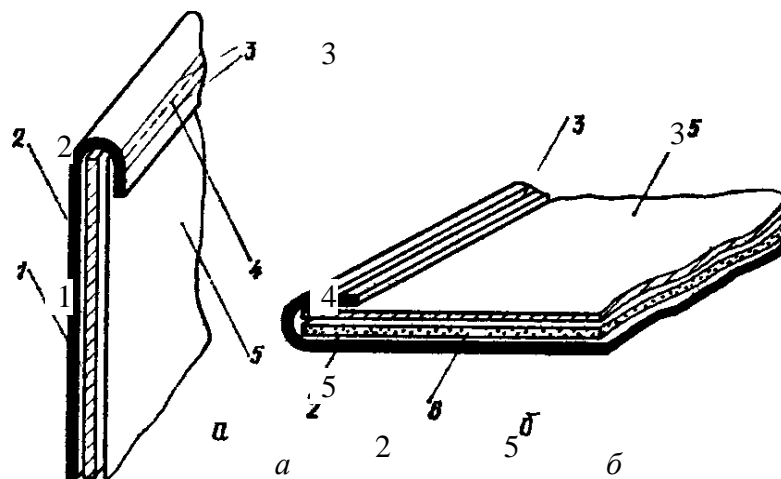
Схеми зварювання деталей СВЧ:
